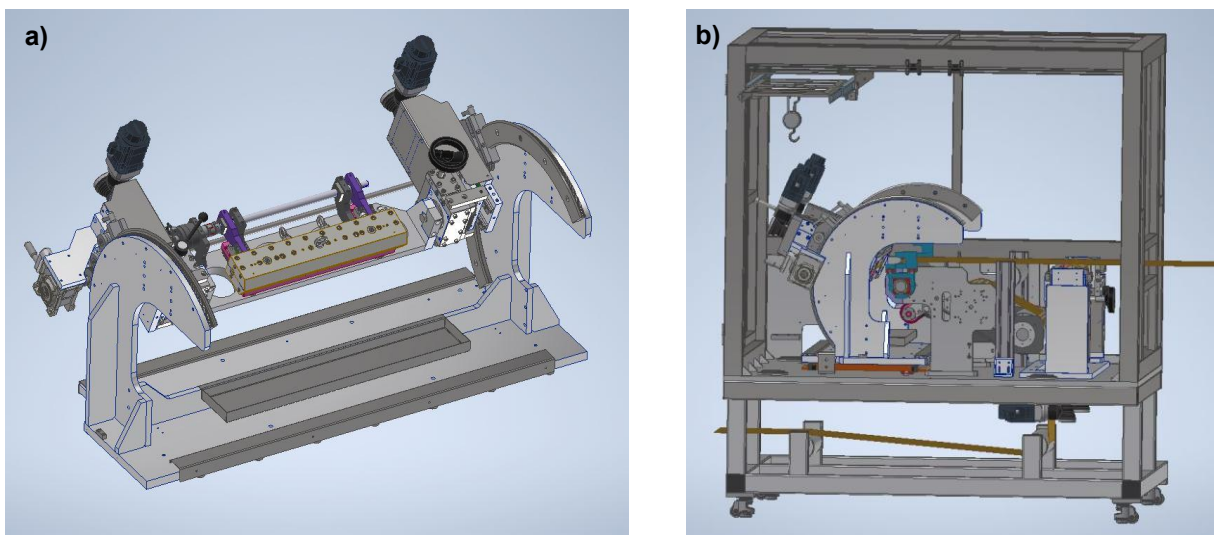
Prototypen-Beschichtungseinheit a) in Detail Ansicht und b) komplettes Modul zur Integration in die Pilotline.
